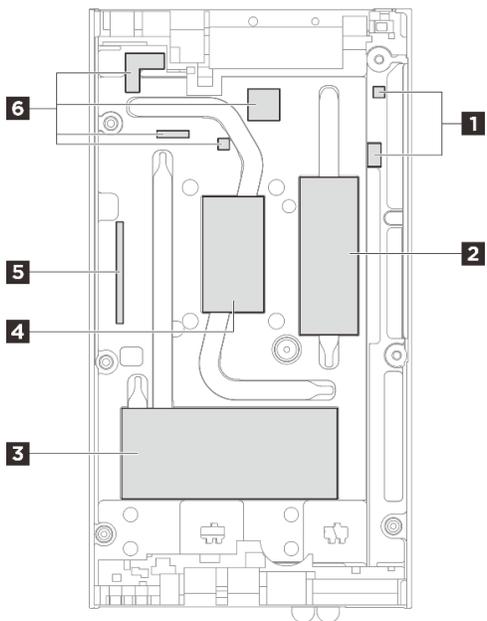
Carter supérieur – Identification et emplacement des kits de tampons thermiques
